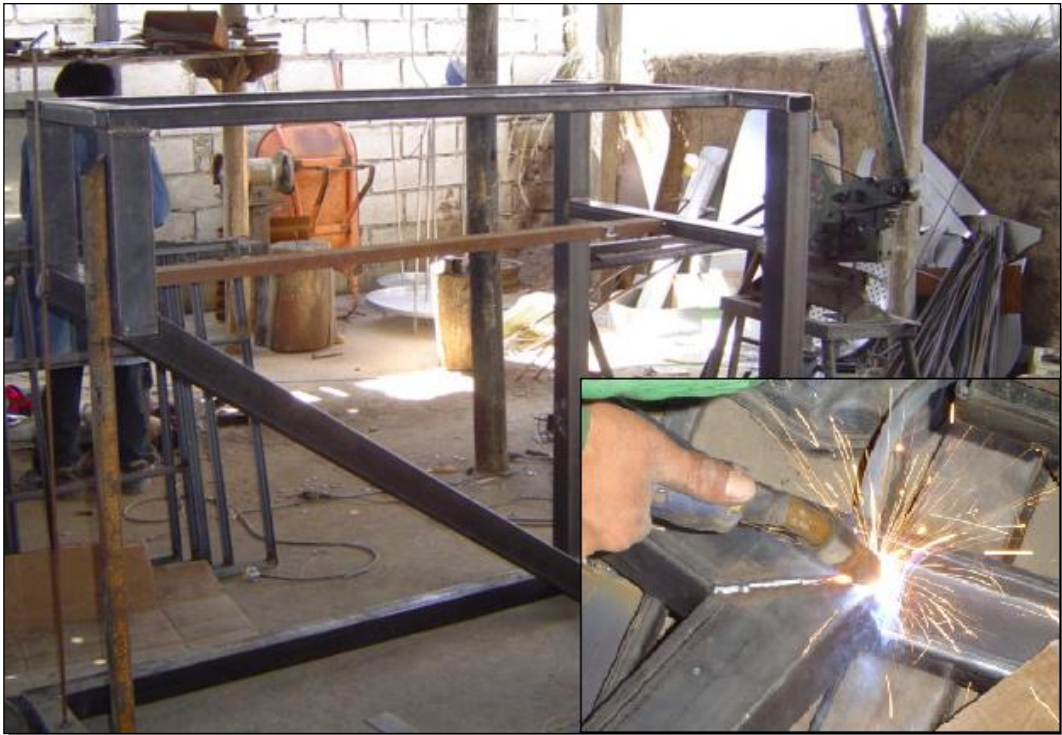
Soldado del soporte del rotor principal con Suelda MIG.
